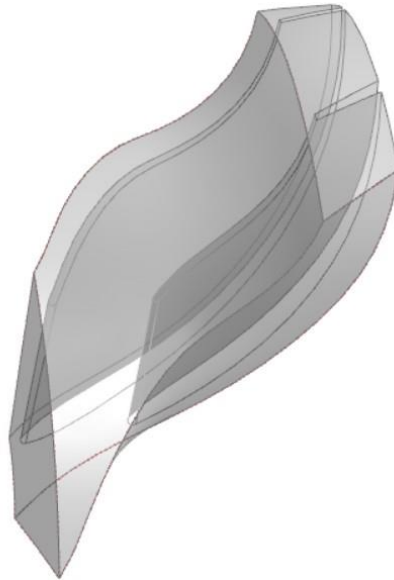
Трехмерная модель проточной части центробежного компрессора
